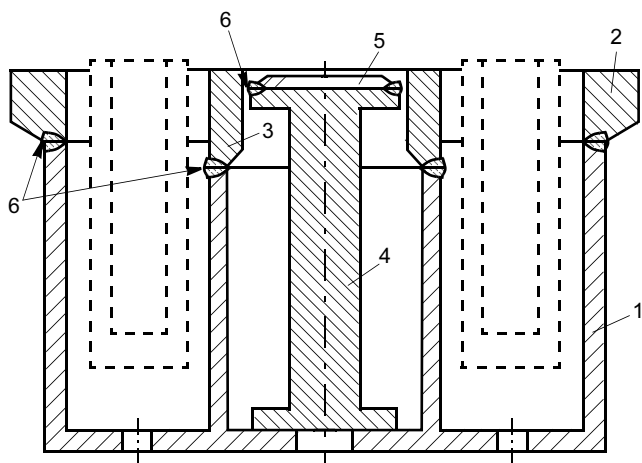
Конструкторско-технологическое решение сварного тонкостенного магнитопровода из стали 10880 с торцевой вставкой из пермендюра 49КФ: 1, 4 — сталь 10880; 2, 3, 5 — пермендюр; 6 — сварные швы
